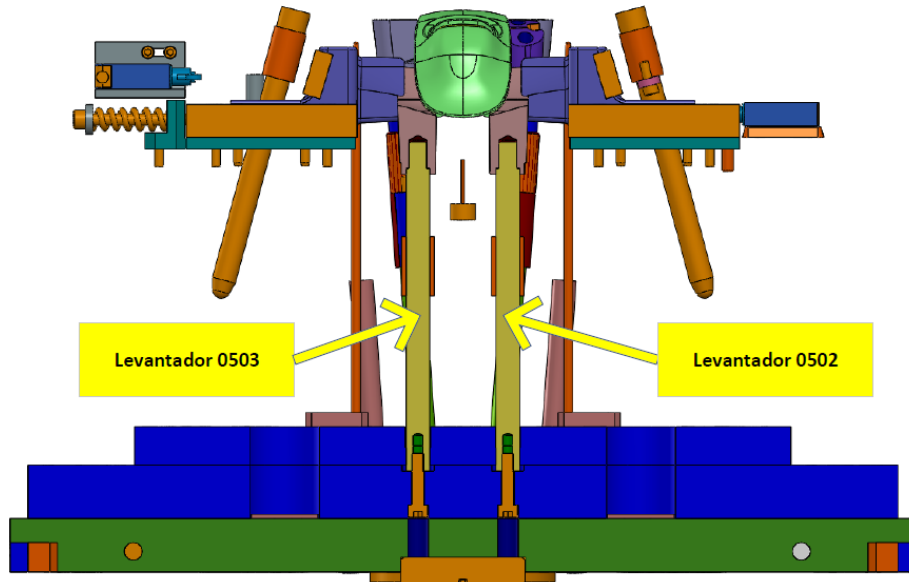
Vista em corte (frontal) dos levantadores verticais a 90°
